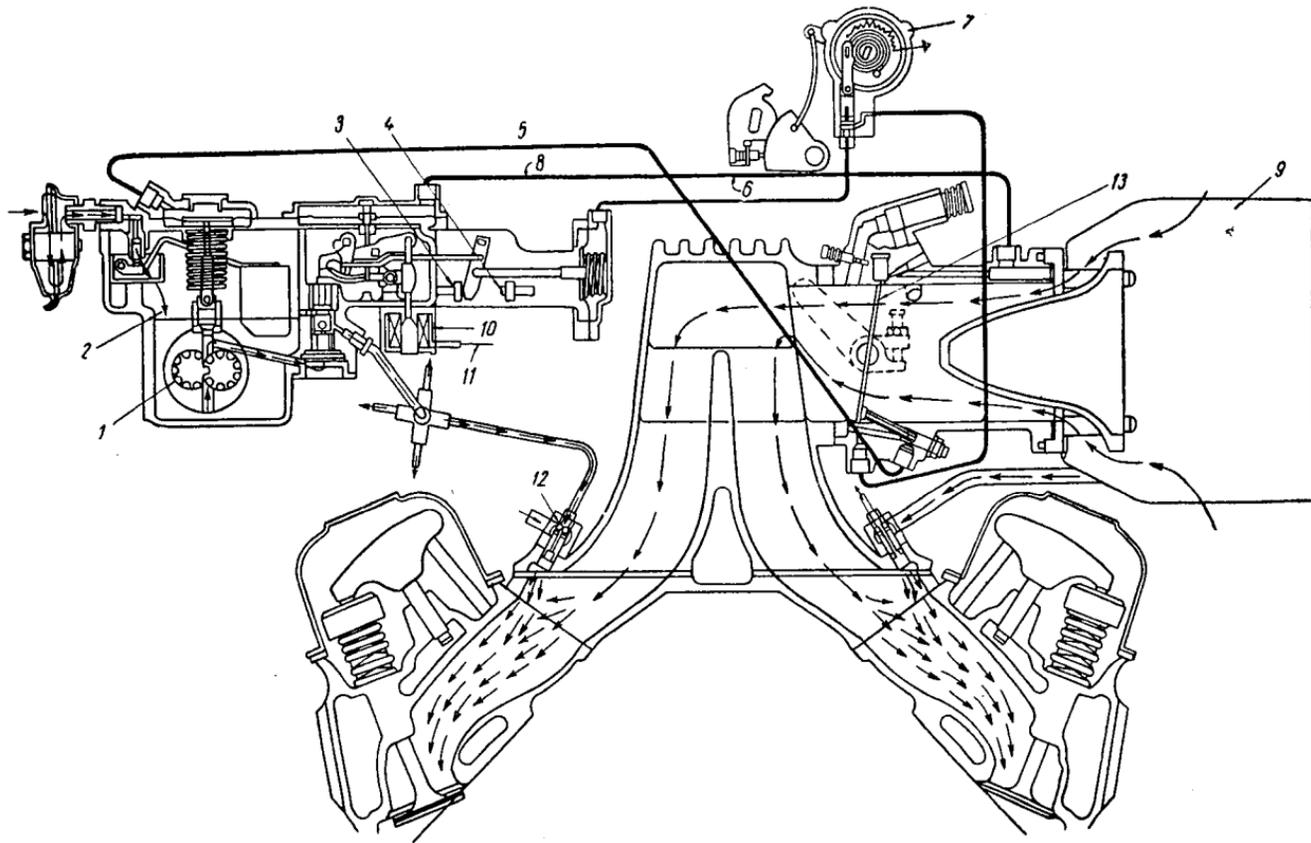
Схема устройства системы впрыска топлива двигателя Chevrolet:
